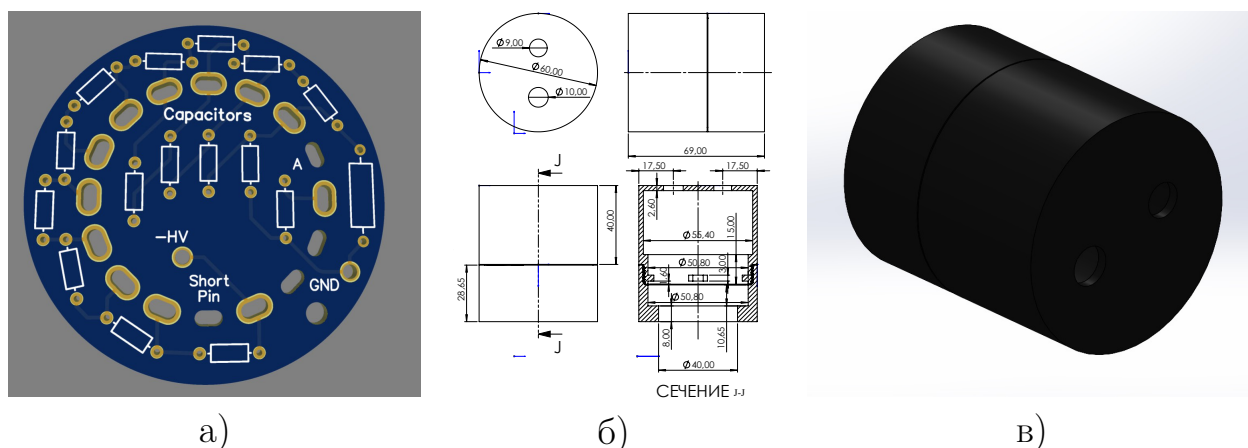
а) Плата делителя напряжения. б) Чертеж корпуса для делителя напряжения ФЭУ. в) 3D-модель детали. В отверстия помещаются BNC- и SHV-разъемы (сигнальный и питания соответственно), а сам делитель напряжения размещается на противоположном торце детали.
